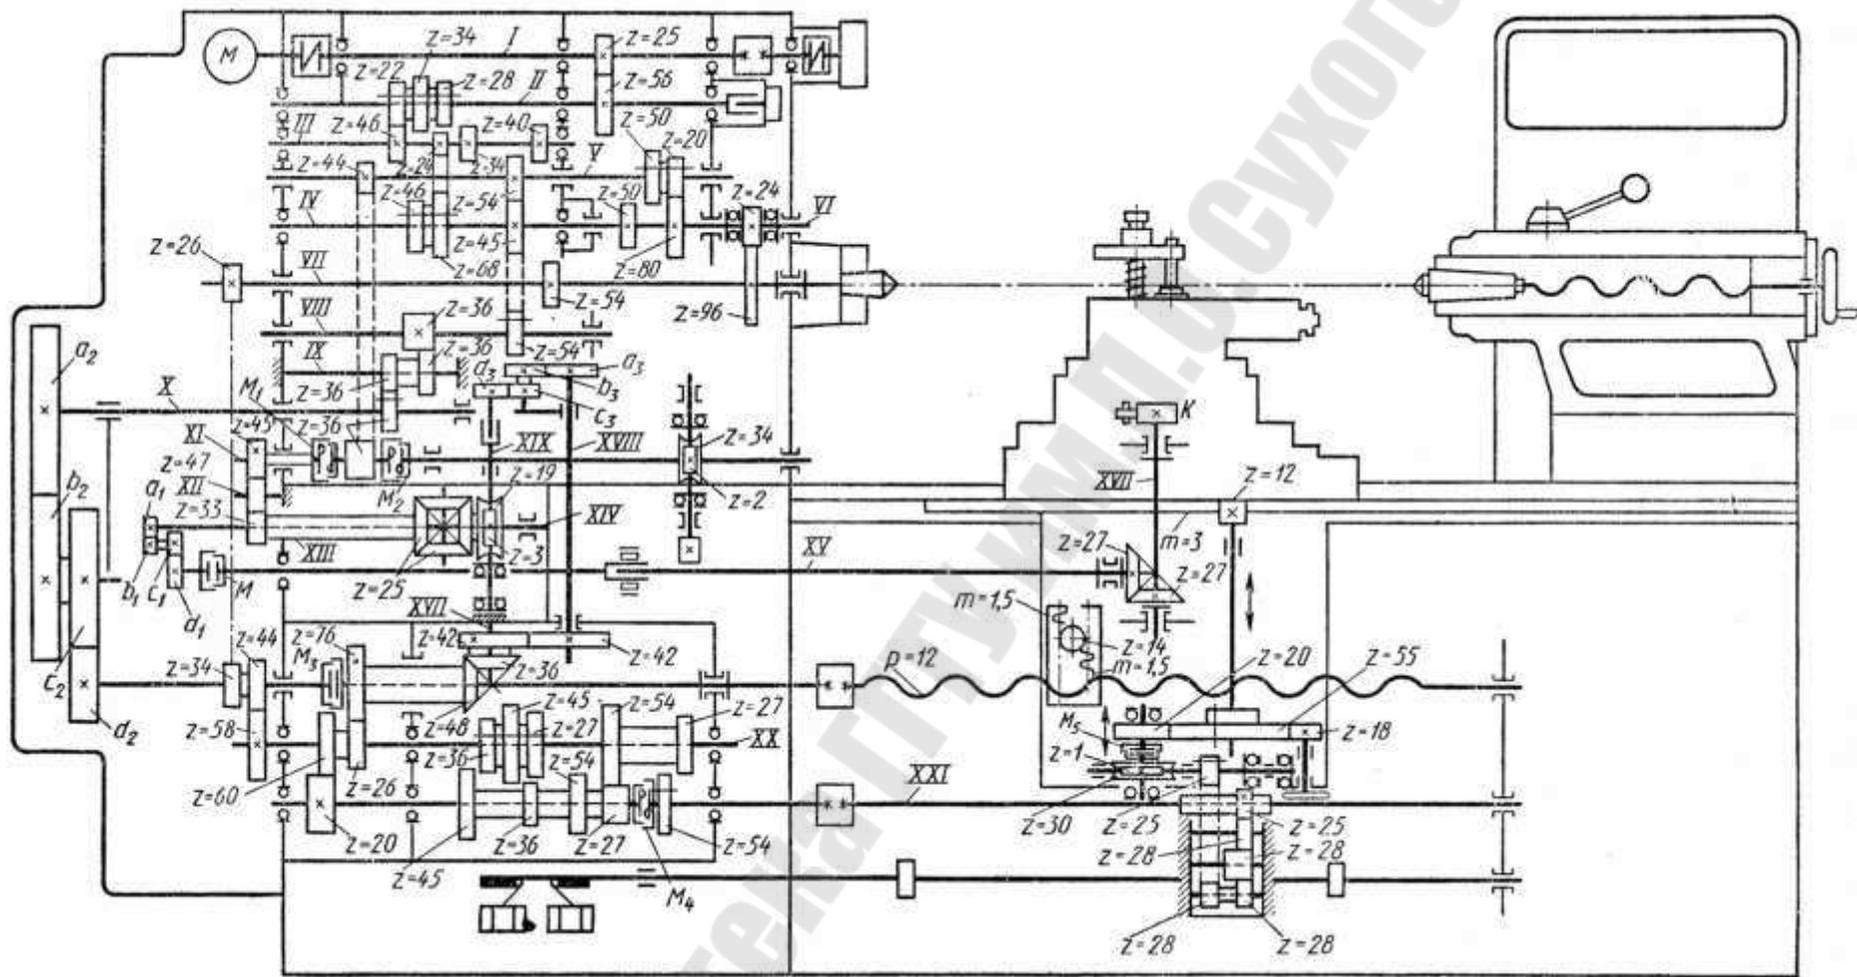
Кинематическая схема токарно-затыловочного станка модели 1Б811
